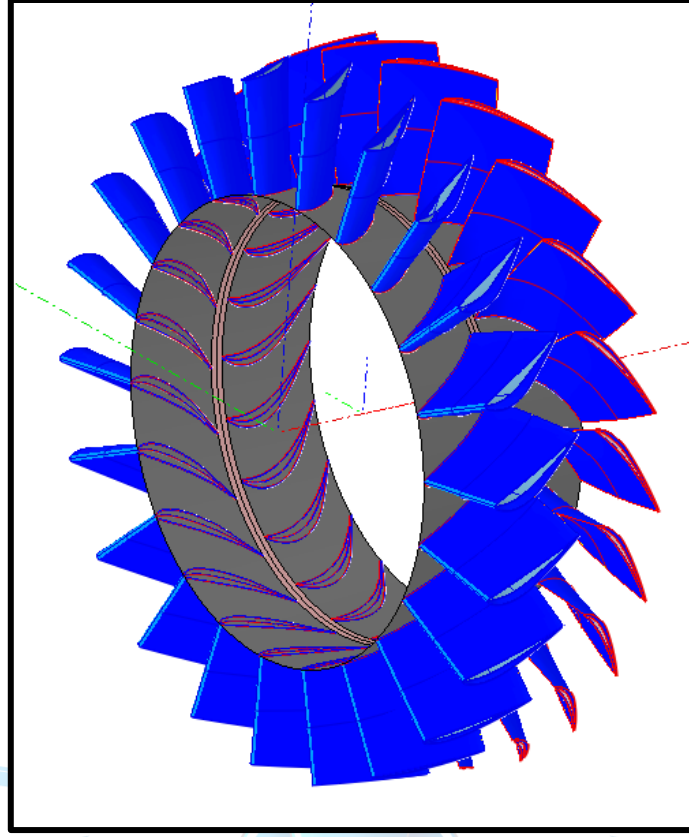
Optimizasyon sonrası rotor ve stator geometrik değerleri
